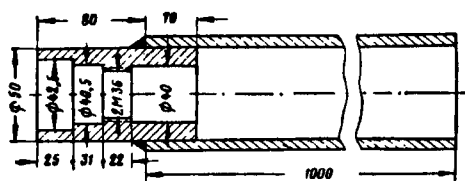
Приспособление для сборки мотор-генератора ДМГ-1 500/50
